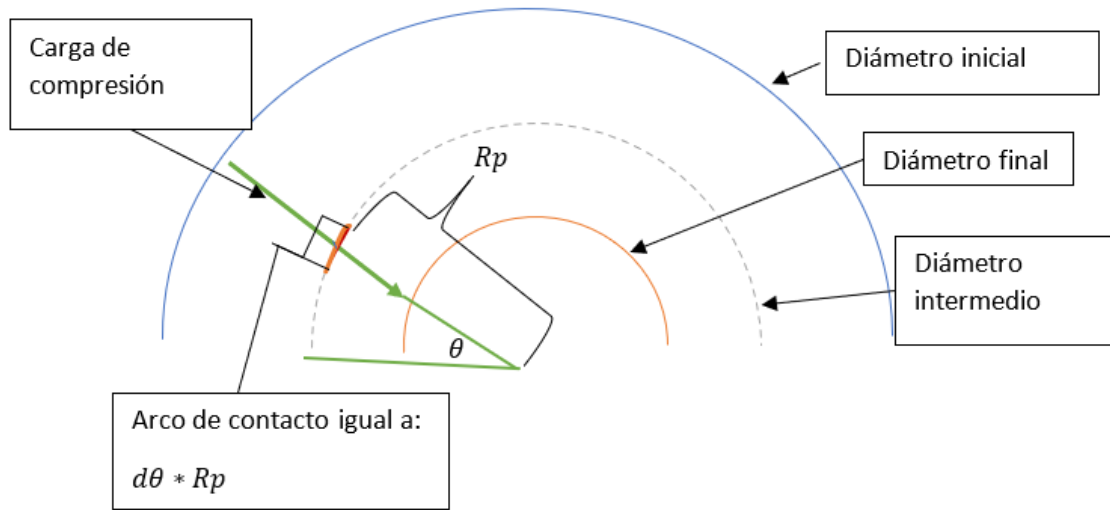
Área de aplicación de la compresión. Fuente: elaboración propia
